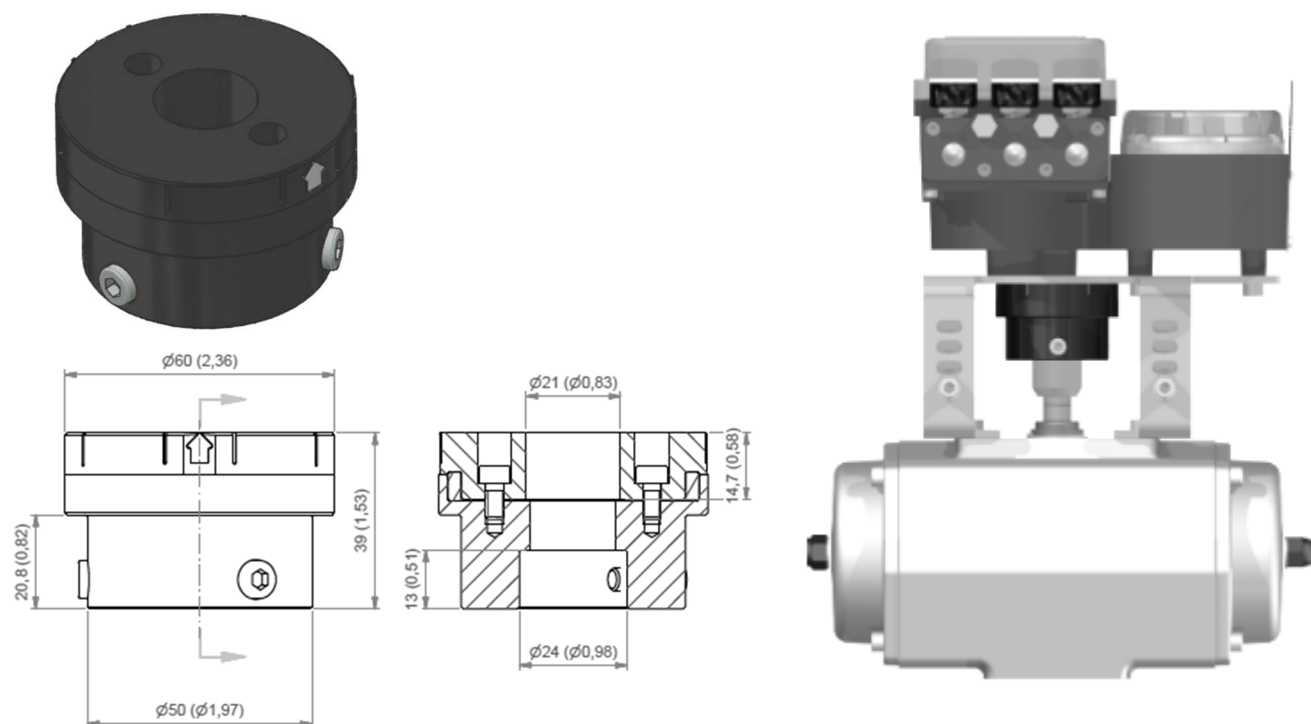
Dimensiones y montaje del imán giratorio.
